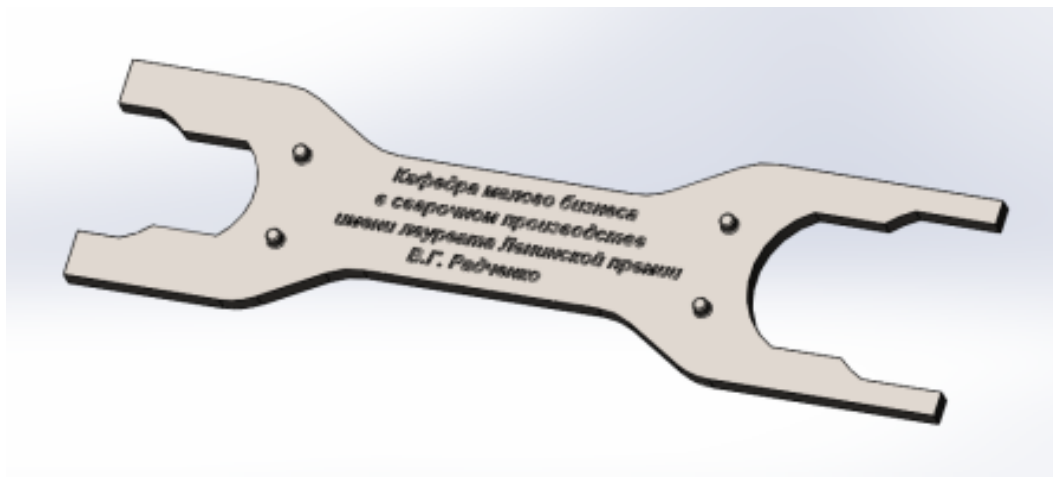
Специализированный ключ для сборки сверхзвукового устройства для наплавки (с гравировкой)
